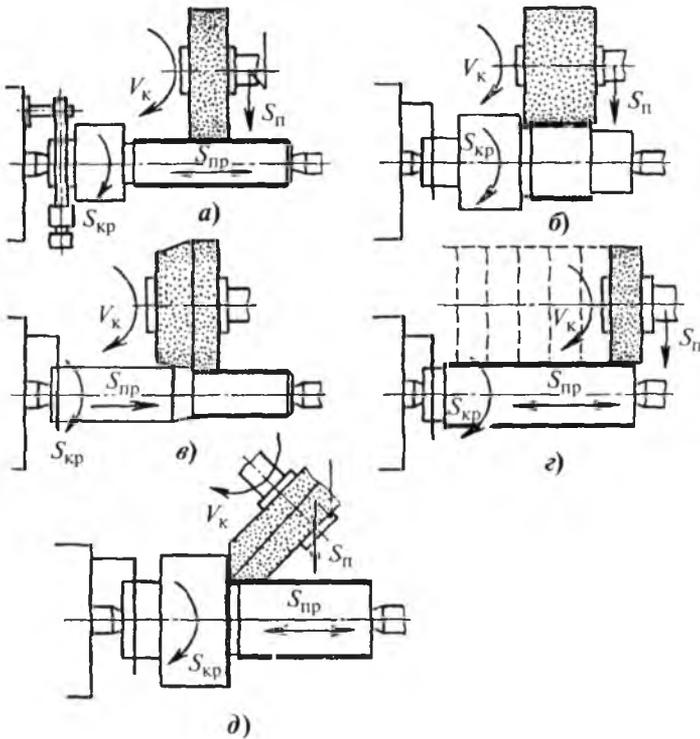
Схемы обработки заготовок на круглошлифовальных станках:
